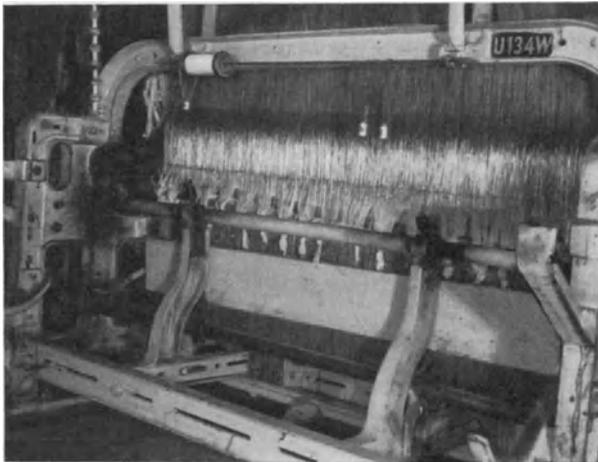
Gewichtskasten zur Führung der Jacquardgewichte.
